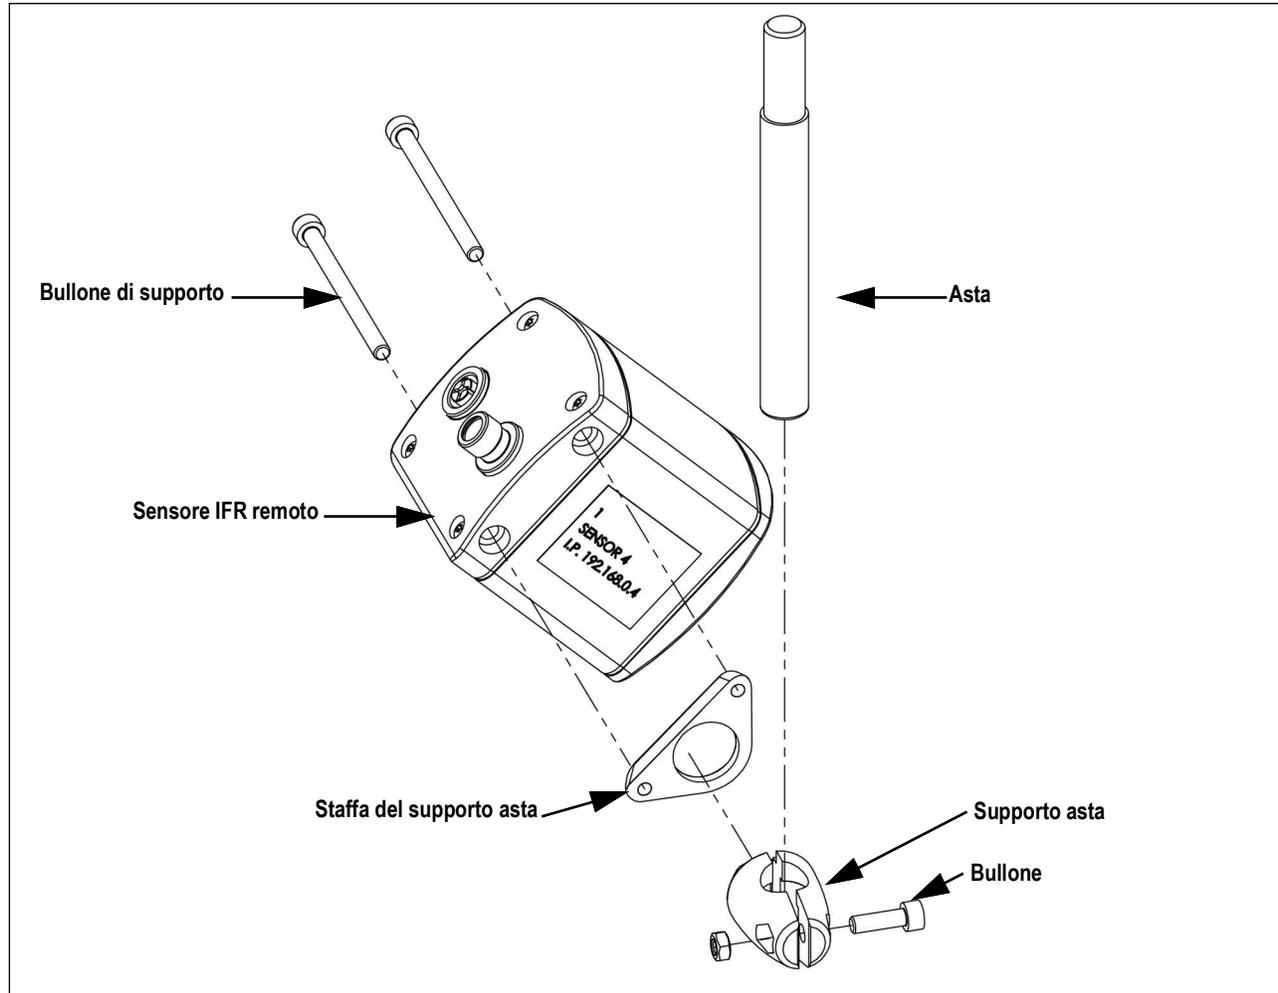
Assemblaggio del gruppo sensori IFM remoti
